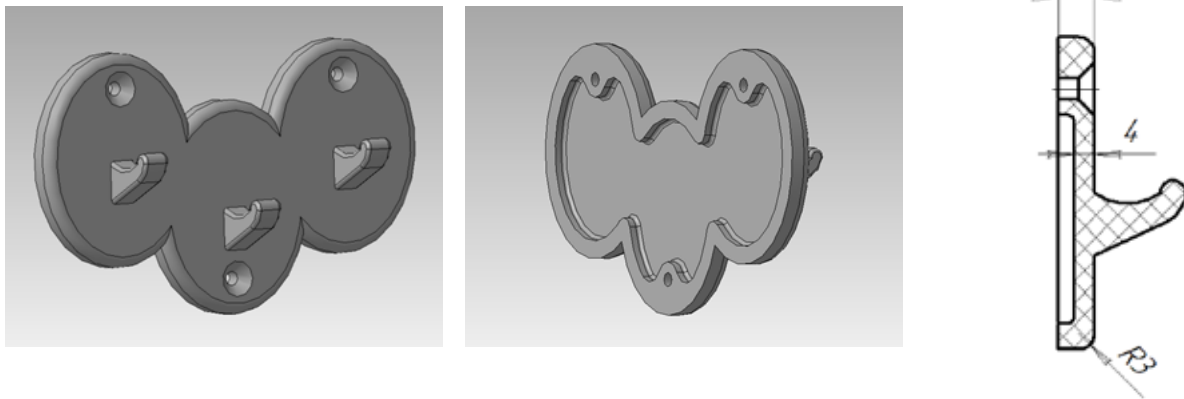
Образец изделия «Крючки для полотенец» и его профильный разрез (по правому крючку)
